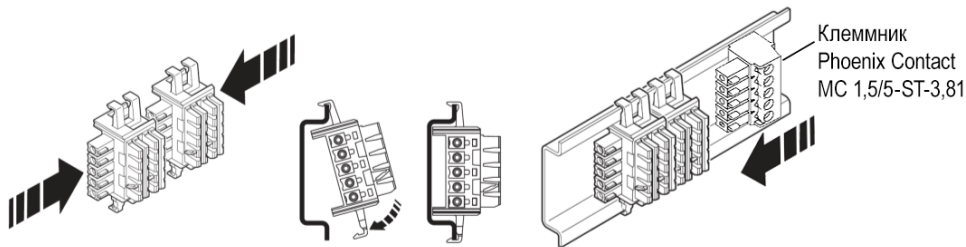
Установка шинных соединителей на DIN- рейку
